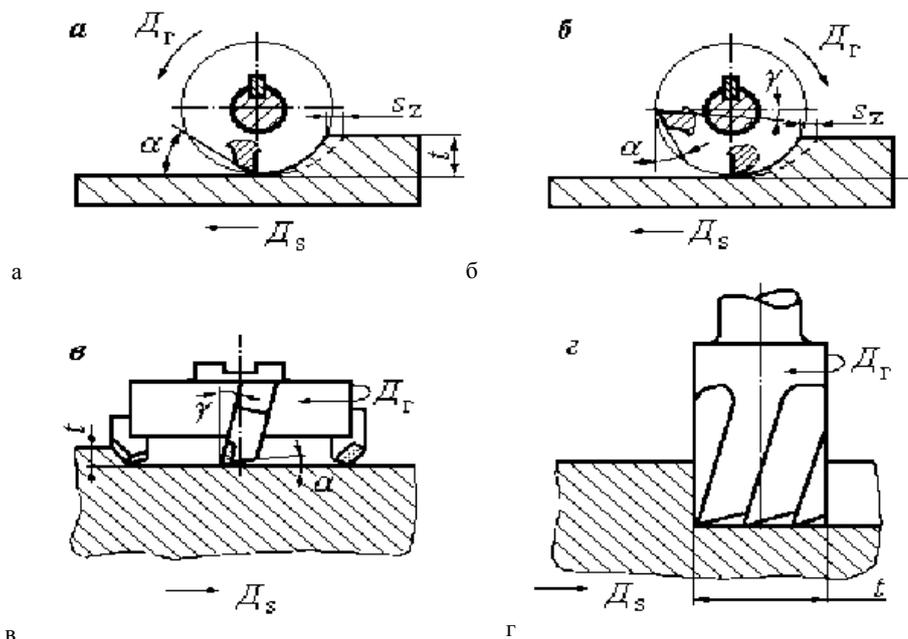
Виды фрезерования: а – против подачи, б – по подаче, в – торцевой фрезой, г – концевой фрезой.
